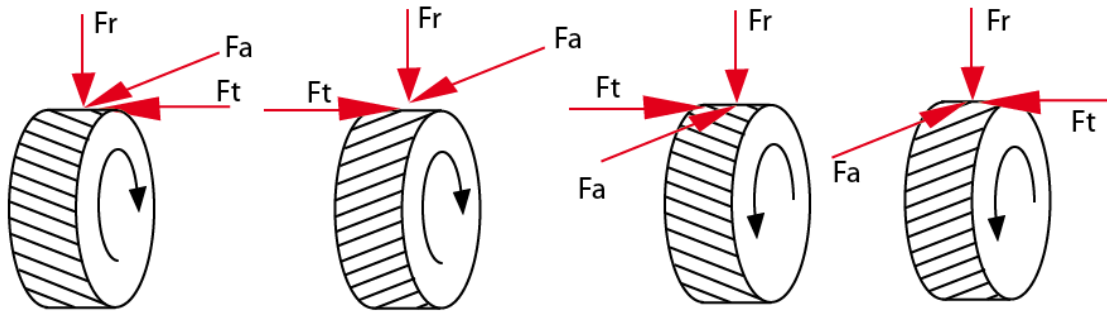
FUERZAS ENGRANAJES HELICOIDALES
